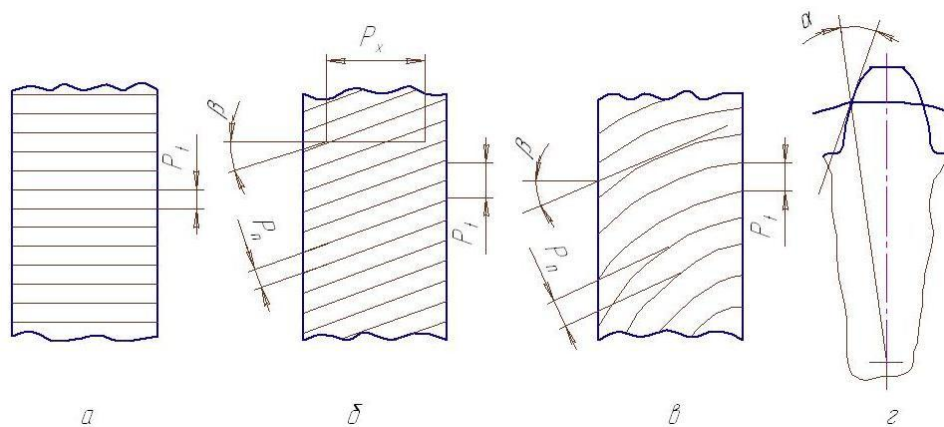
Форма та розміщення зубців зубчастих коліс
